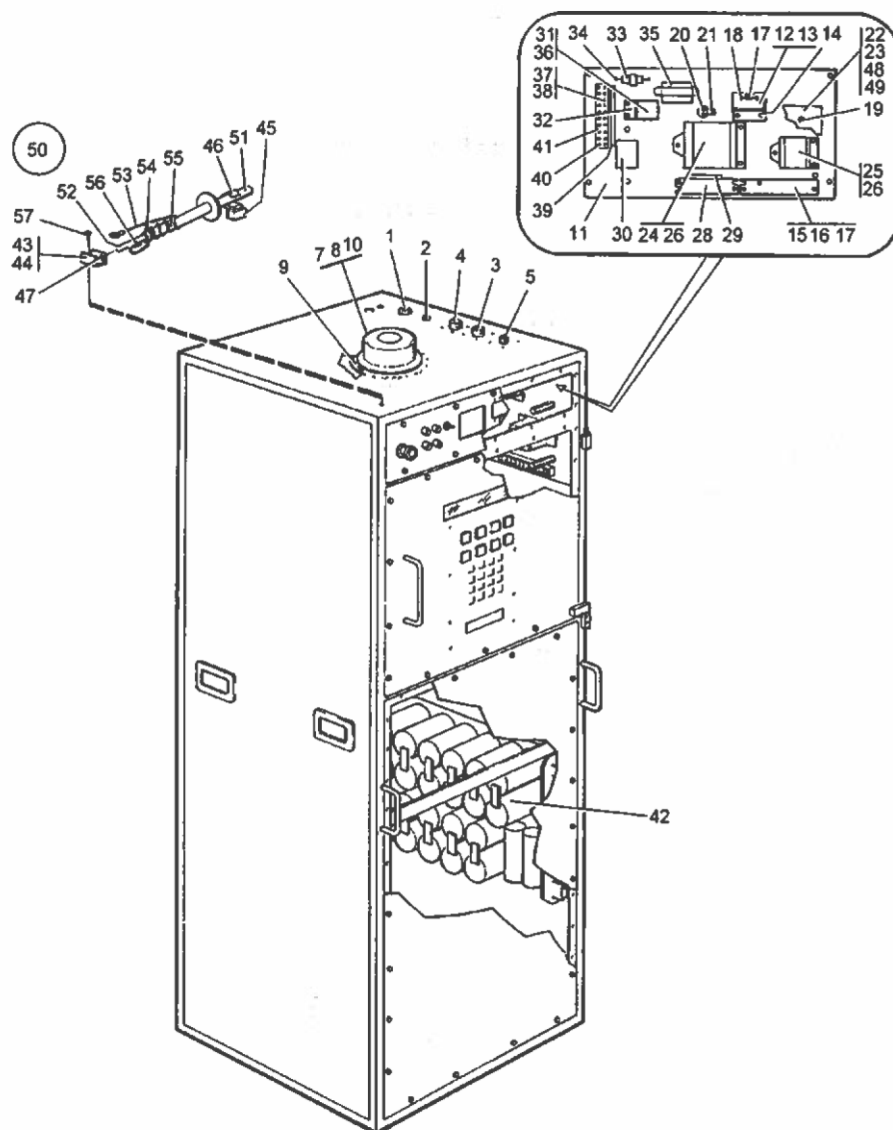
Placeringsteckning. Förenkling av mindre detaljer
